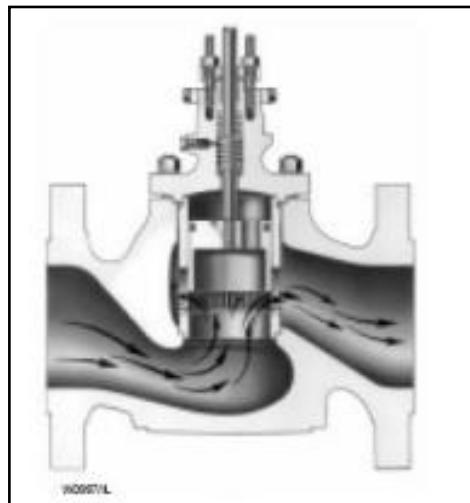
Ballanced-Plug Cage-Style Valve Bodies
